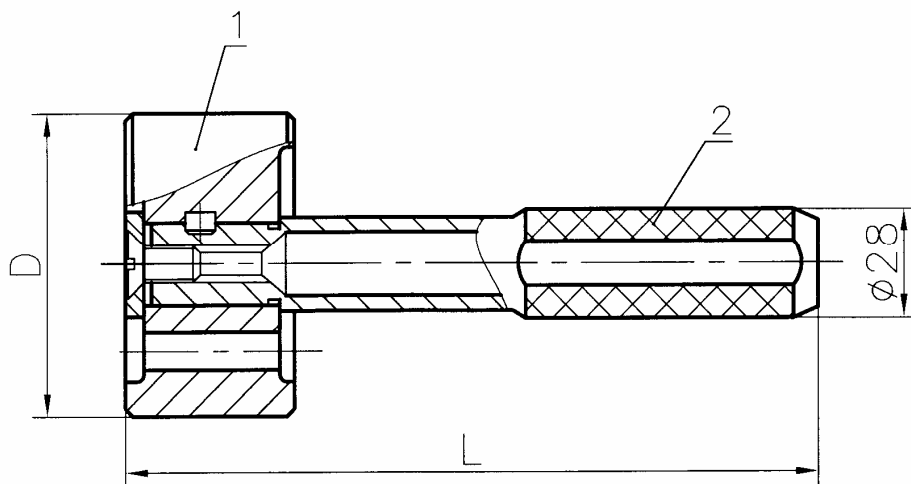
Калибр-пробка непроходной с насадкой:
